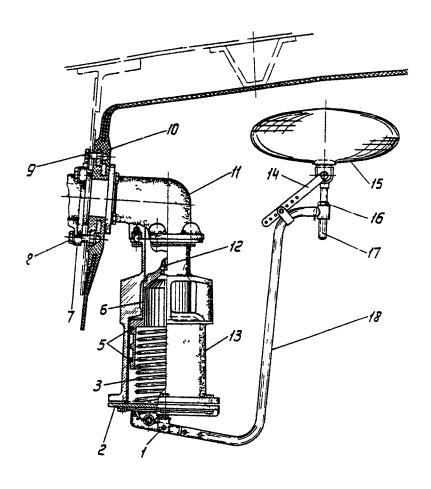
Установка предохранительного поплавкового клапана в баках # 4.
